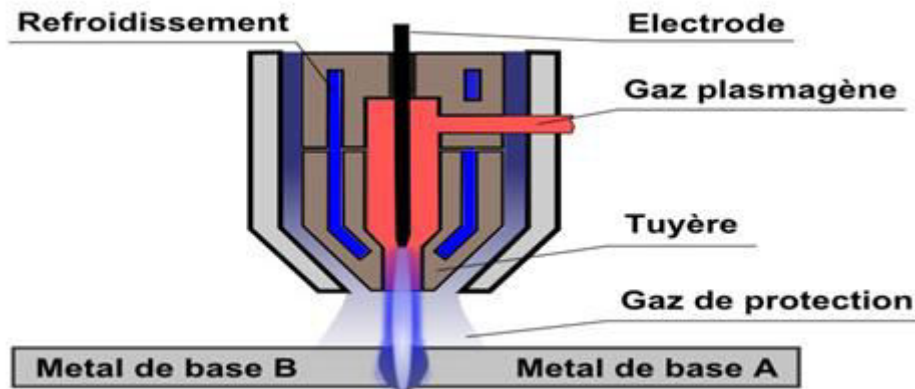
Schématisation du principe du soudage par plasma
